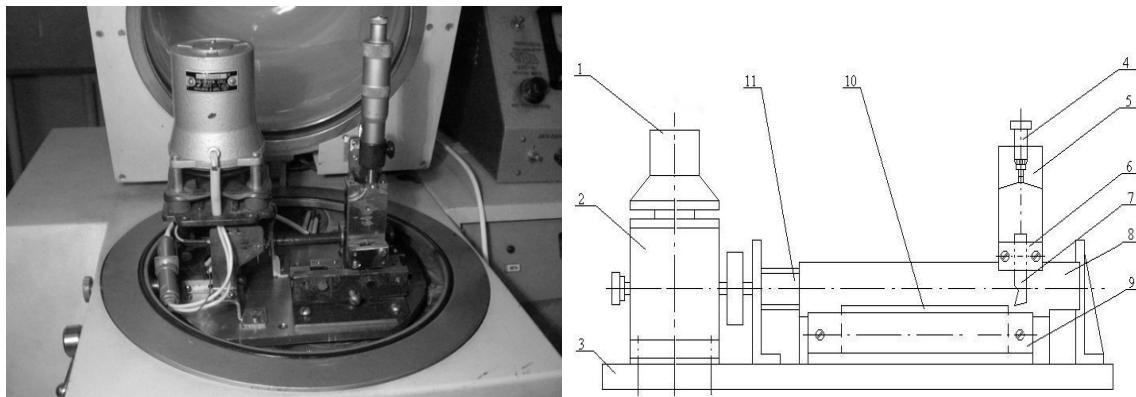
Внешний вид (а) и схема установки (б) для резания
